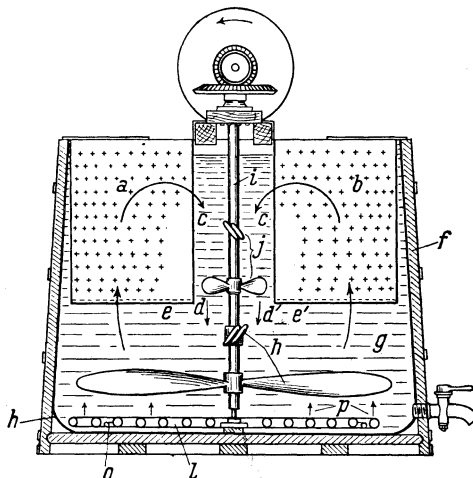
Mischmaschine der „Société française de Construction des Machines pour Tannerie“
